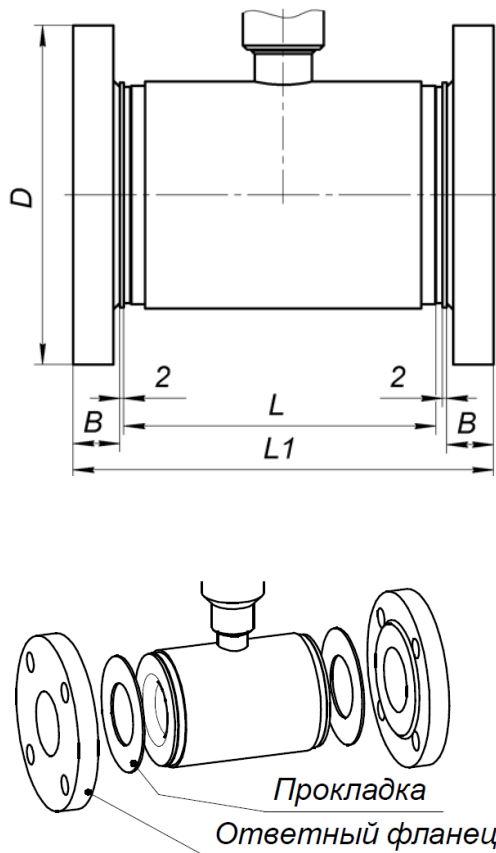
Габаритные размеры сборки расходомера вместе с ответными фланцами ГОСТ 33259-2015 (без колец заземления).
